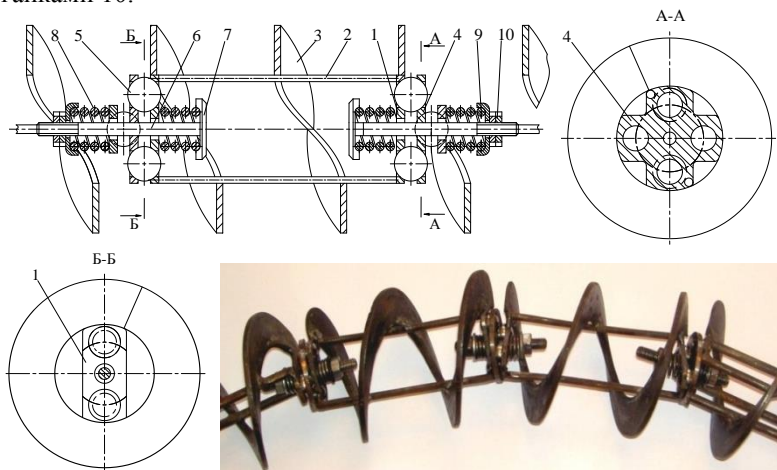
Конструктивна схема та загальний вигляд шарнірного робочого органу гвинтового конвеєра
